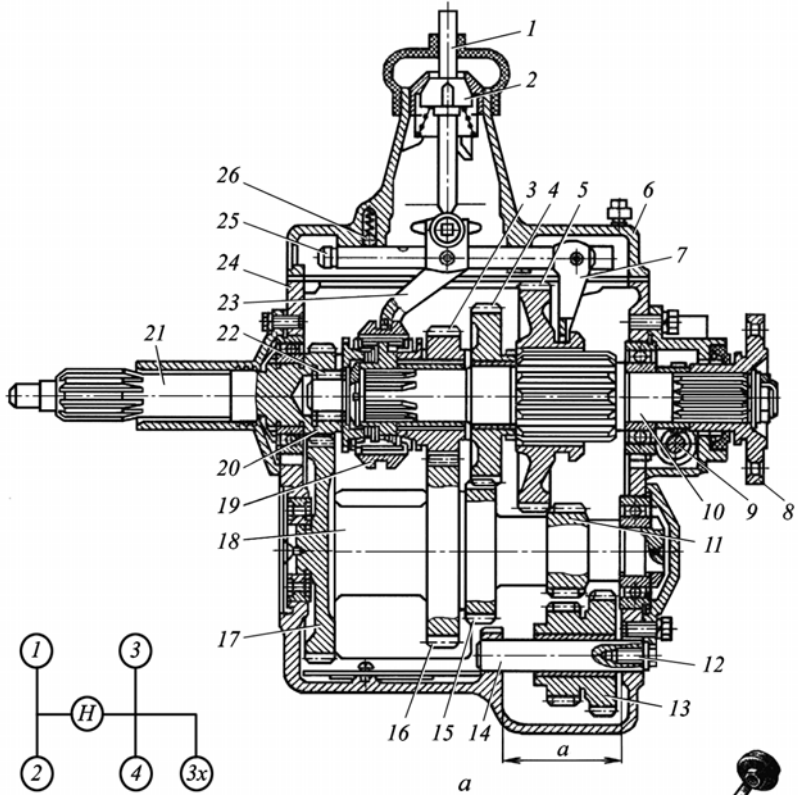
Коробка передач автомобіля ГАЗ-3307:
